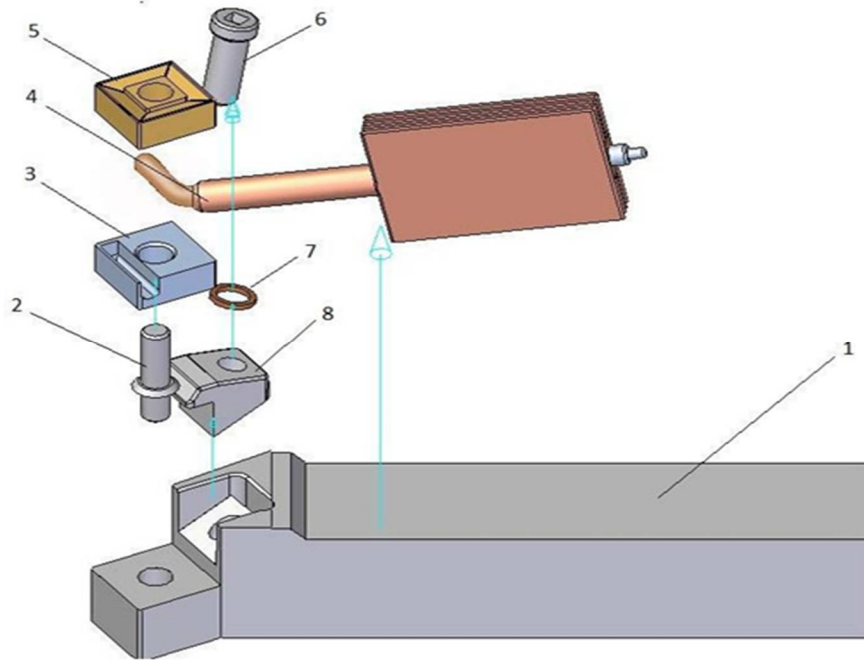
Конструкція різця з тепловою трубою (1 – державка; 2 – штифт; 3 – опорна пластина; 4 – тепла труба; 5 – ріжуча пластина; 6 –гвинт; 7 – шайба; 8 – прижим-стружколом)
